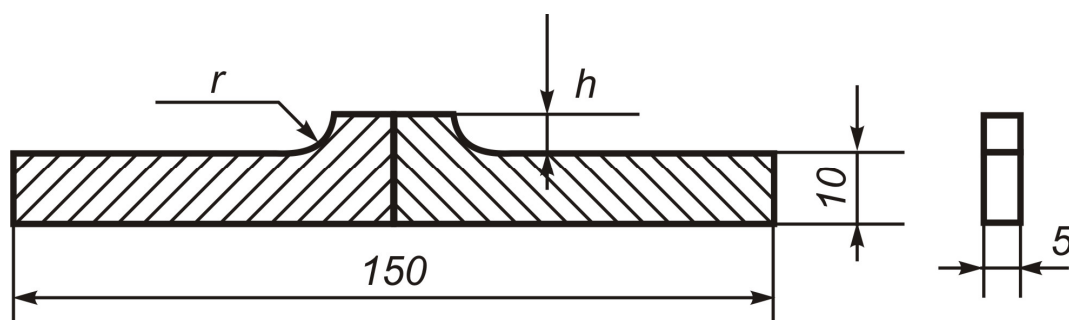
Конструкція зразка для дослідження на опір втоми з контролем росту тріщин та поперечний шліф зварного з'єднання
